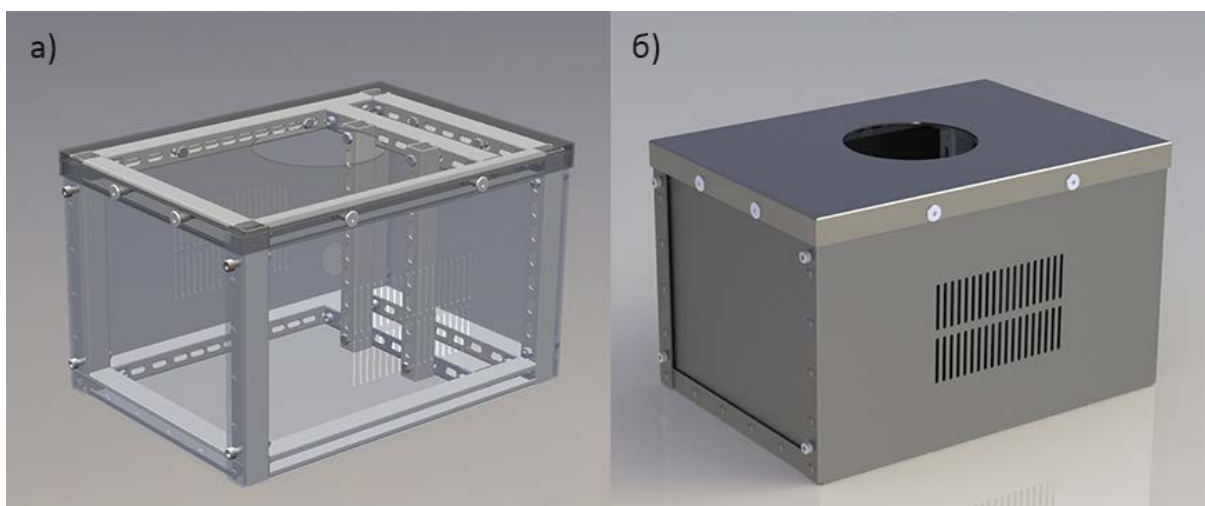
а) Рендер корпуса с прозрачными стенками;
